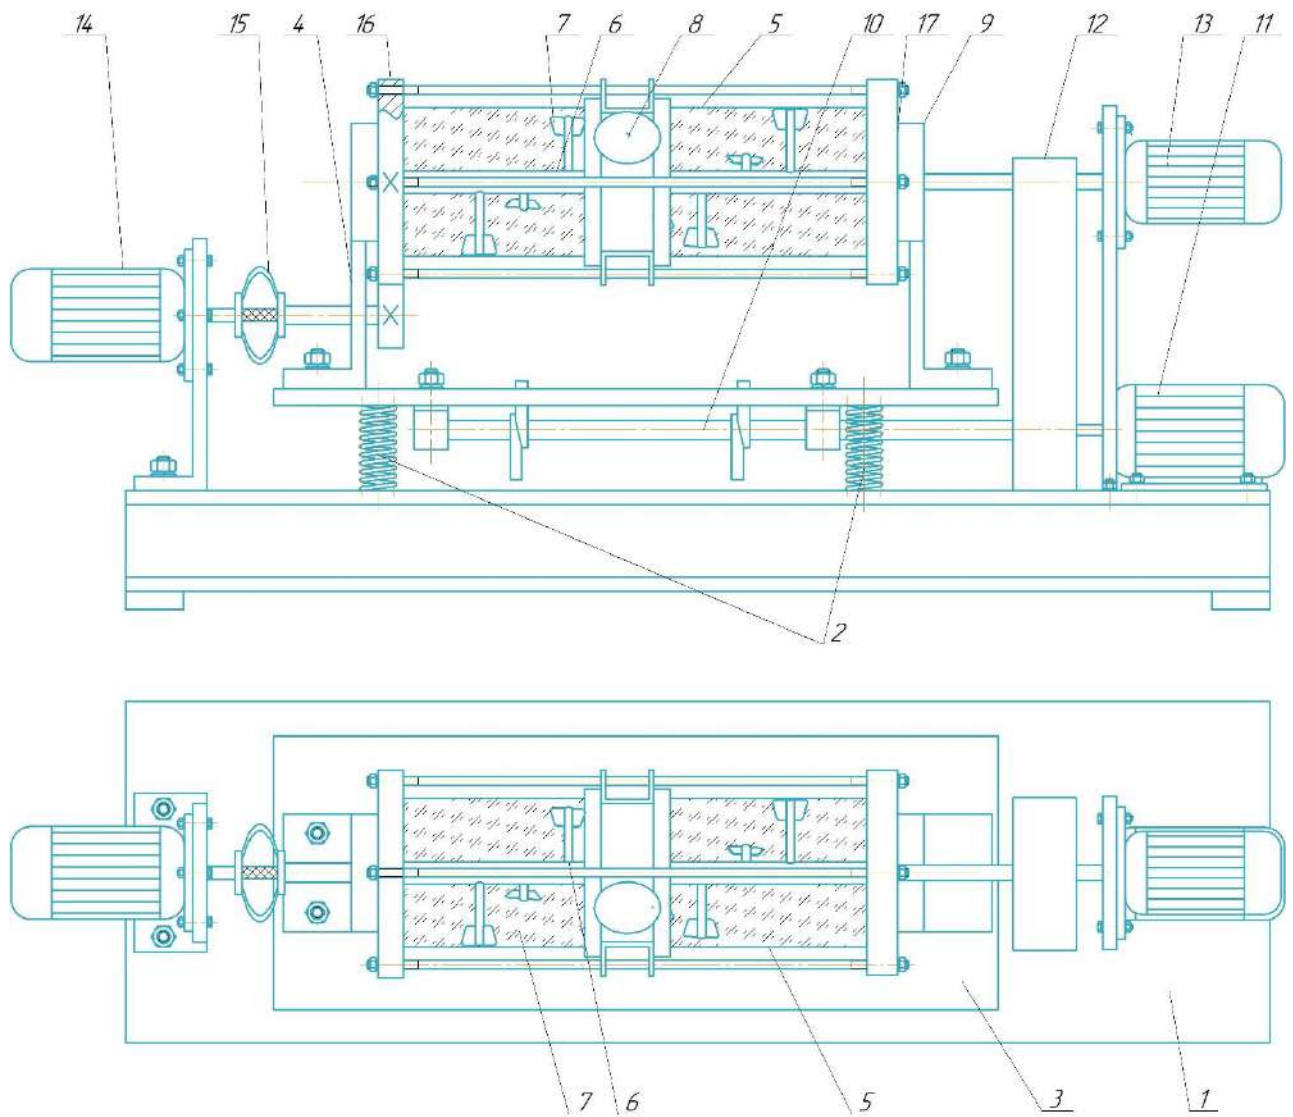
Схема вібраційного змішувача: 1 – рама; 2 – пружинна підвіска; 3 – платформа контейнера; 4 – опора; 5 – корпус змішувача; 6 – лопатевий вал; 7 – лопаті; 8 – завантажувальний люк; 9 – підшипниковий вузол; 10 – віброзбуджувач; 11, 14 – електродвигун; 12 – захист; 13 – мотор-редуктор; 15 – еластична муфта; 16 – зубчаста передача; 17 – отвори для взяття проб
